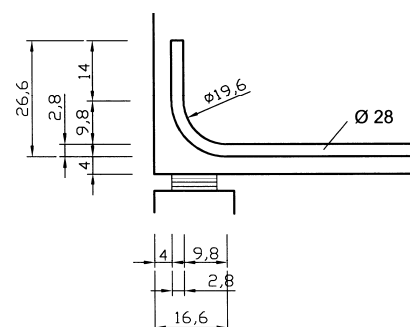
Lage der Schweißung bezüglich der Biegestelle
